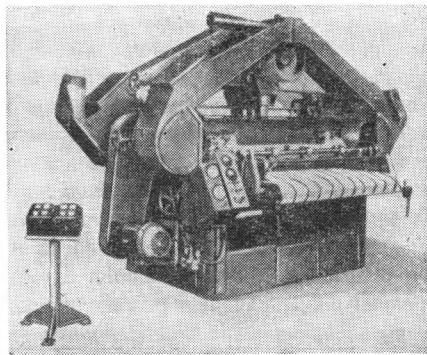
Двухленточный шлифовальный автомат фирмы «Böttcher & Gessner»
